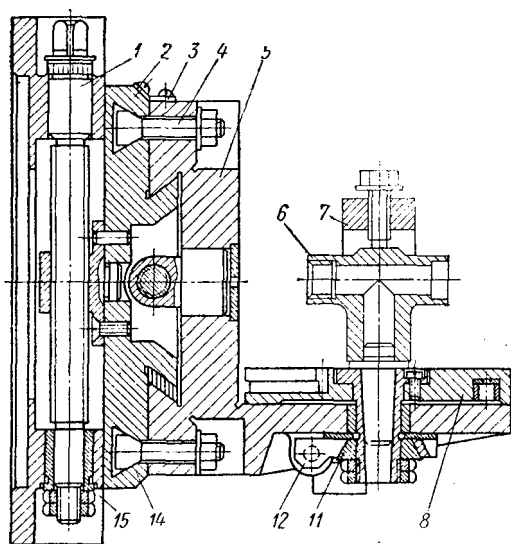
Универсально-перенастраиваемое приспособление для обработки тройников, цапф, крестовин и других деталей на токарных и револьверных станках
